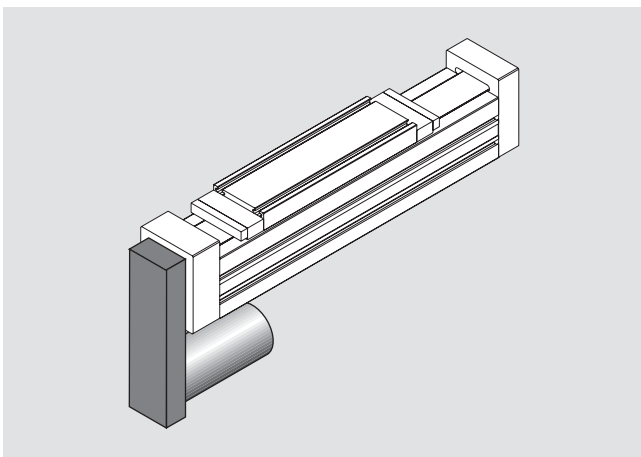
Spindeltrieb mit seitlichem Motoranbau unten (Montagezustand 07)
